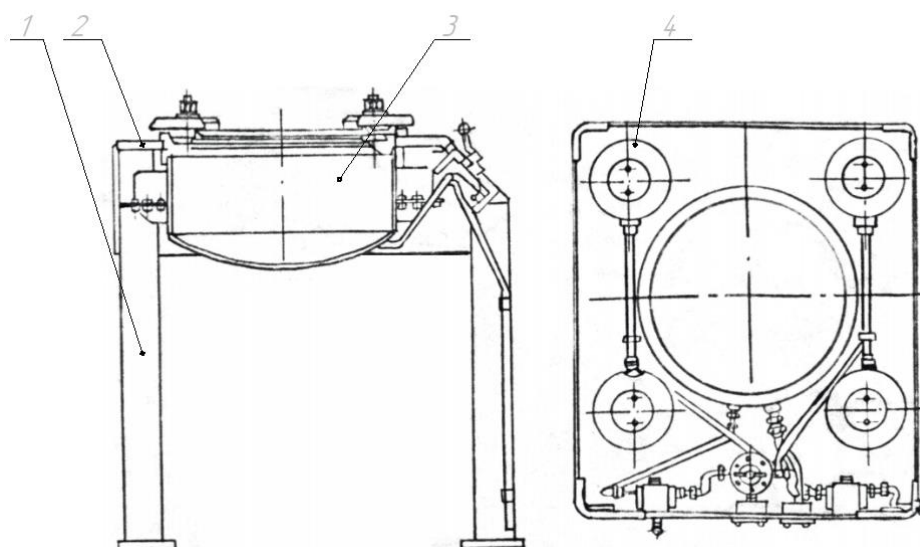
Стенд для испытания главной передачи заднего моста, модель С 416-722
